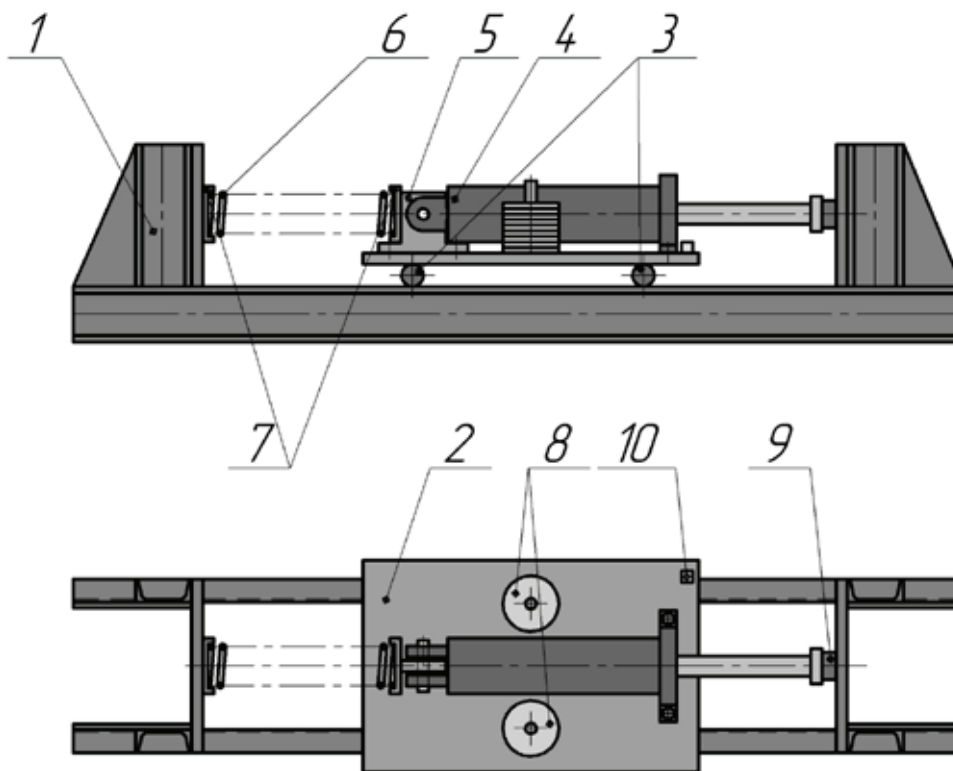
Схема механической части экспериментального стенда: 1 — рама; 2 — подвижное основание; 3 — ролики; 4 — гидроцилиндр; 5 — стойка; 6 — пружина; 4 — стаканы; 8 — грузы; 9 — измеритель силы; 10 — акселерометр
